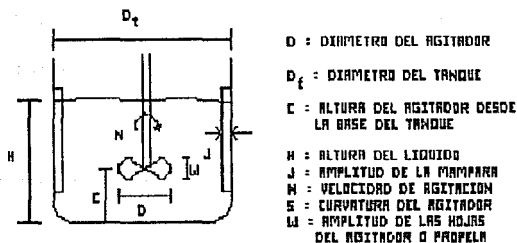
DIMENSIONES DEL AGITADOR
